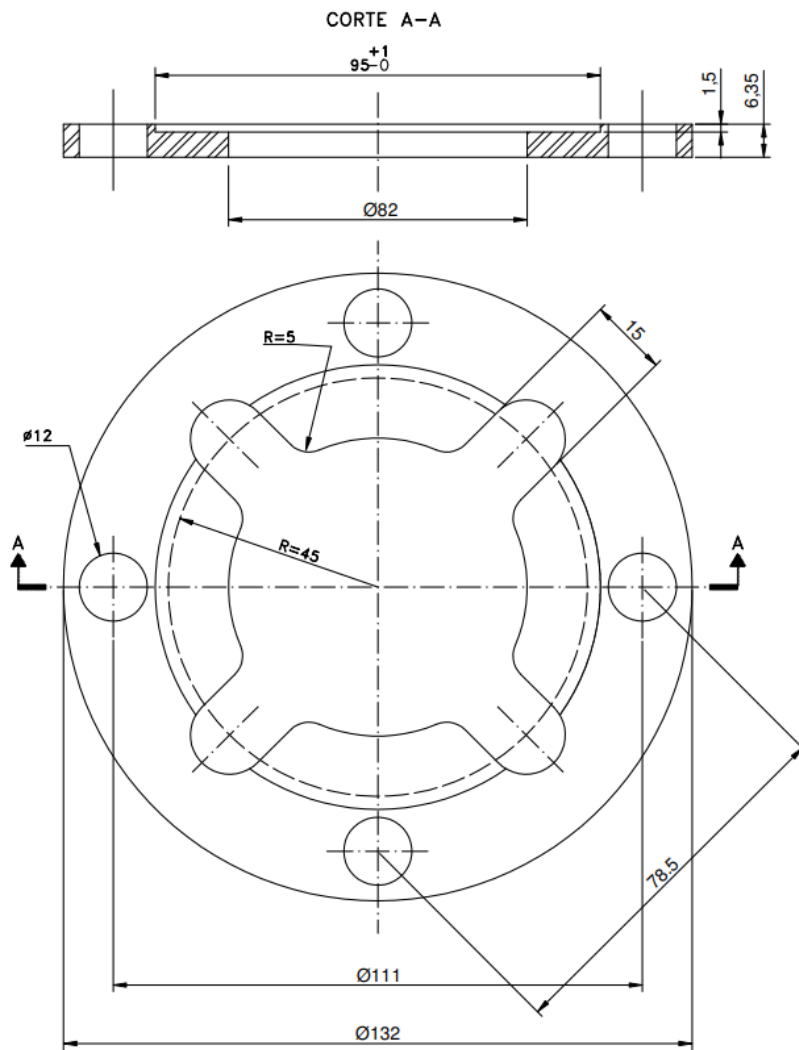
Flange para fixação da bucha de cavidade de inserção (RD/RT)
